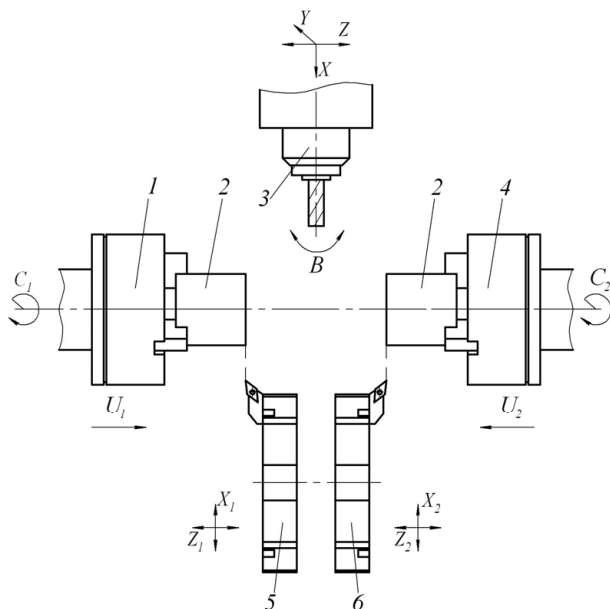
Схема обработки на многофункциональном токарно-фрезерном центре серии МТ: 1 — главный шпиндель; 2 — заготовка; 3 — фрезерная головка; 4 — противопиндель; 5, 6 — револьверные головки
